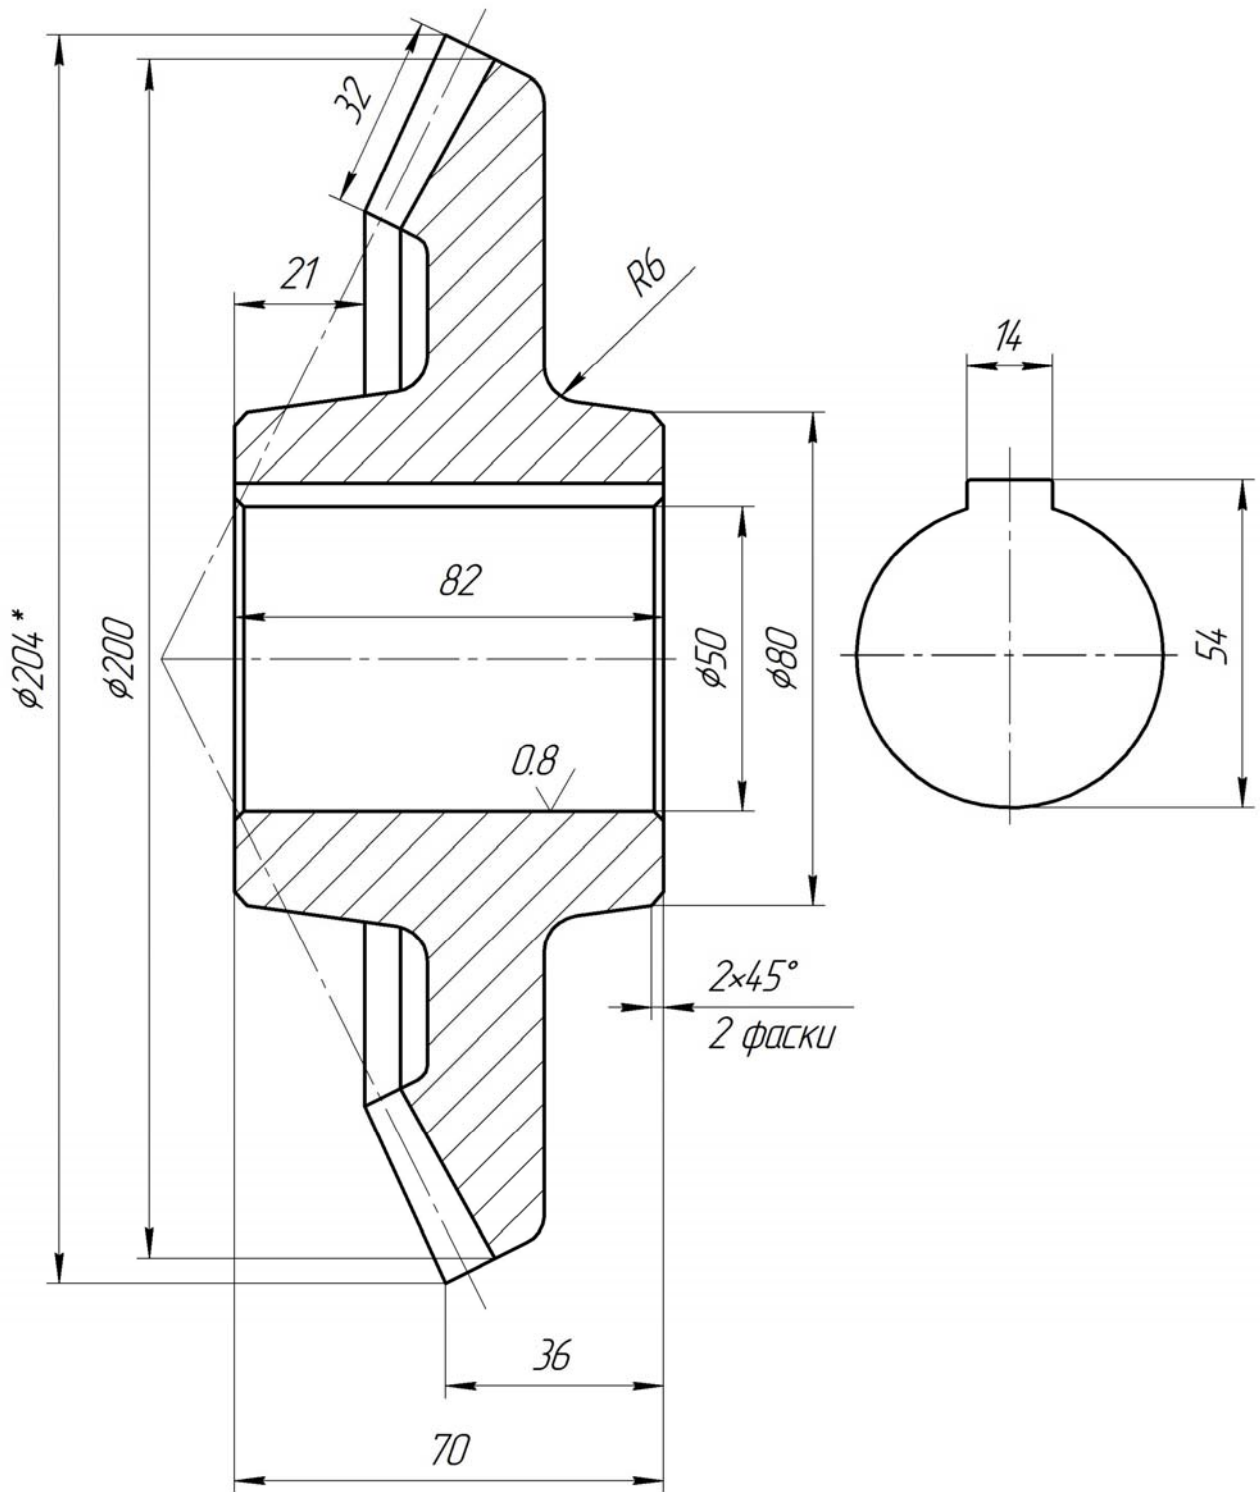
Ескіз конічного зубчастого колеса
